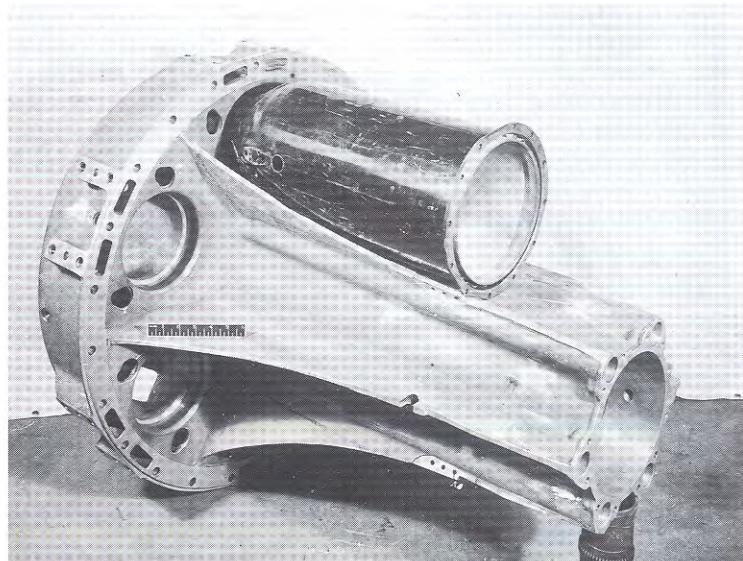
Литая центральная деталь двигателя Юнкерс 109-004 В-1
